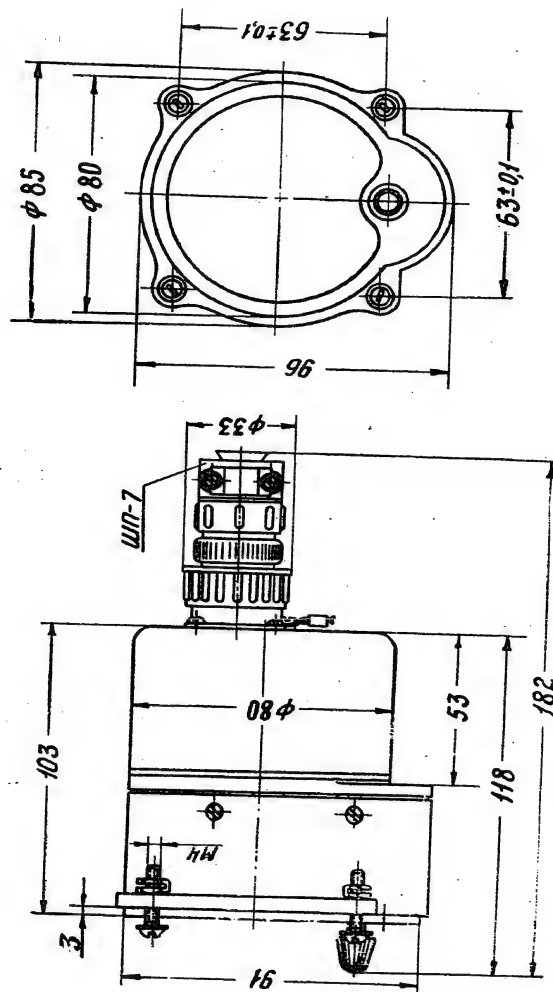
Габаритные размеры показывающего прибора РТМС0,85-Б1
